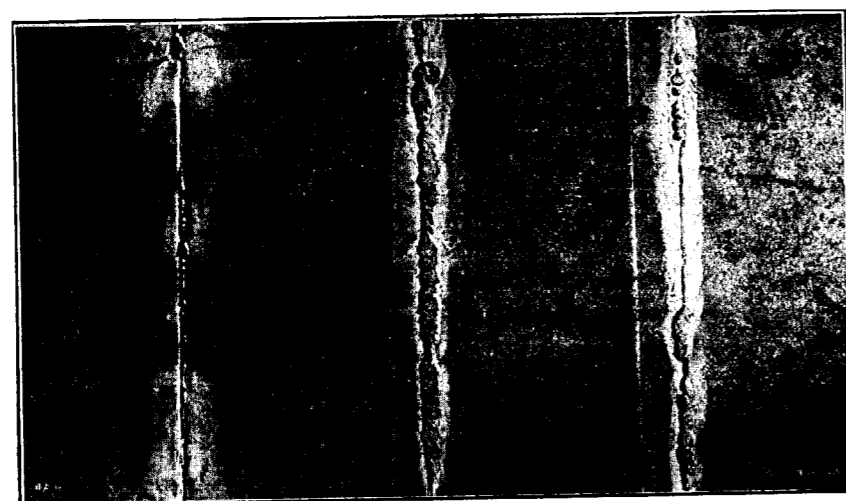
a—Vista anterior de costuras de soldadura en chapa de hierro de 7 mm. de grueso.
